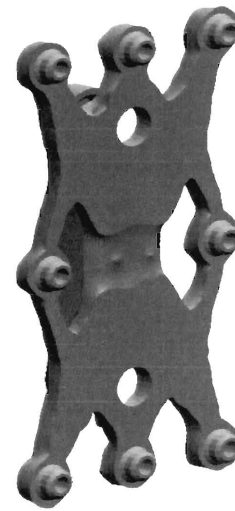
Vedere izometrică element de prindere optimizat topologic CAD – TIP 2
